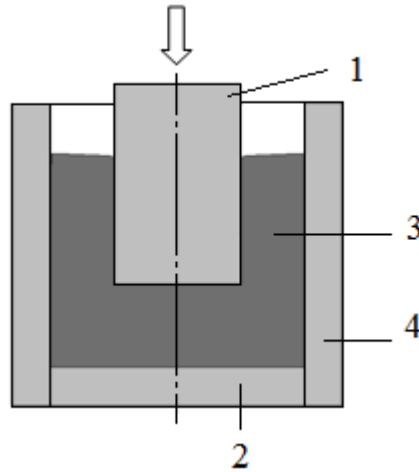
Схема обратного выдавливания: 1 - пуансон; 2 - выталкиватель; 3 - порошковая заготовка; 4 - матрица
